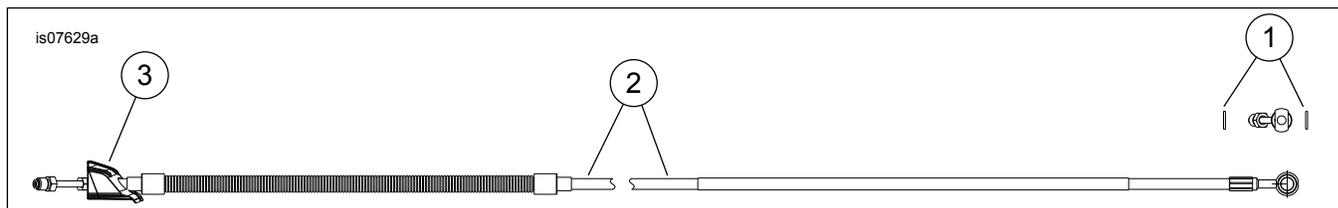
Peças de reposição: Kits de tubulação da embreagem hidráulica
